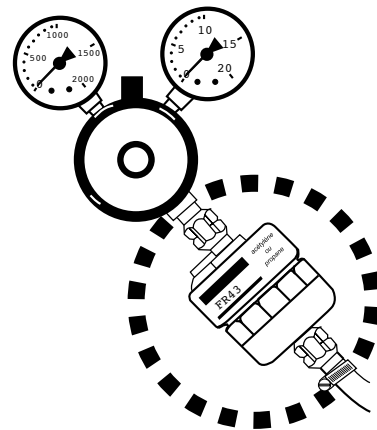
Installation d'un clapet antiretour de gaz et de flamme au niveau de la sortie du détendeur d'une bouteille avant le raccordement au tuyau
